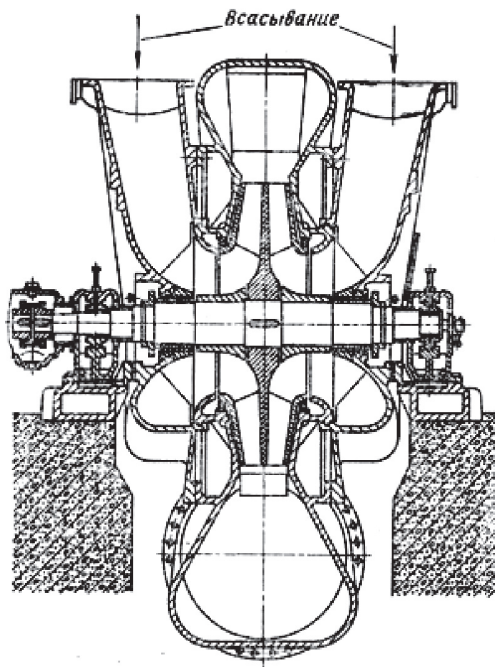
Одноступенчатый нагнетатель с двусторонним колесом
